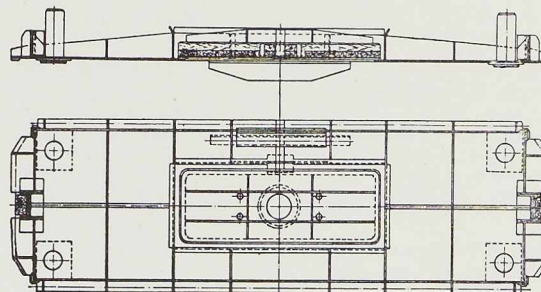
Clapet d'aérage d'une cage construite en 1937.
